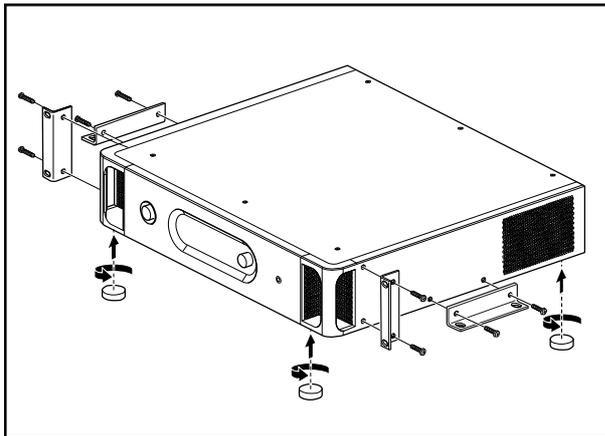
Передатчик с опциональными монтажными кронштейнами и ножками для настольного использования
